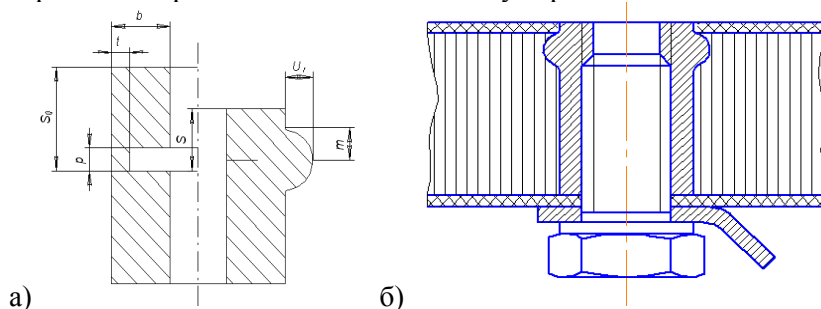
Конструкция вкладыша (а) и конструкция соединения «вкладыш-трехслойная конструкция» (б).
